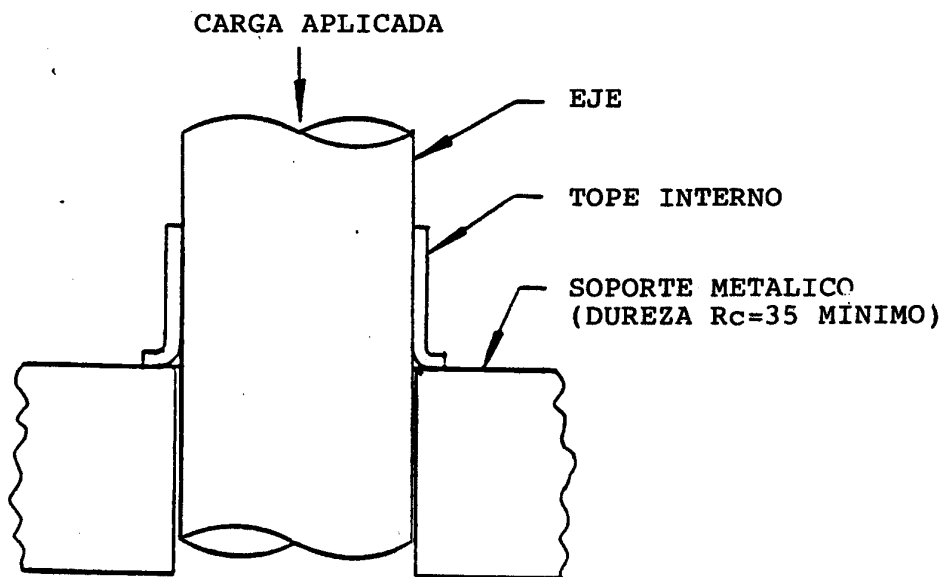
Esquema típico del dispositivo de ensayo para resistencia estática de la soldadura.
